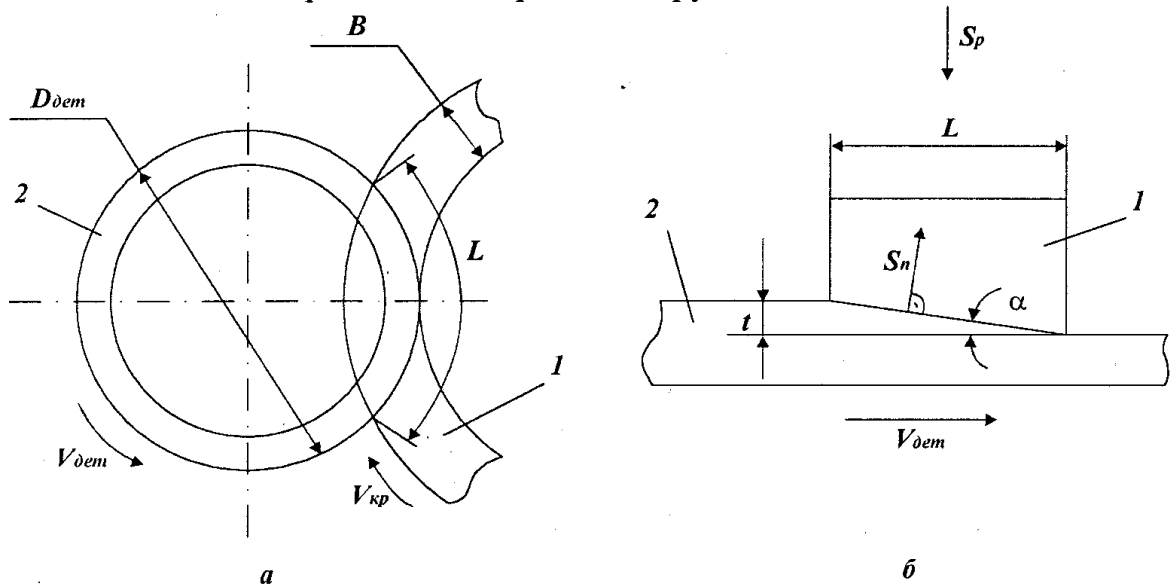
Расчетная схема шлифования: 1 - круг; 2 - деталь
